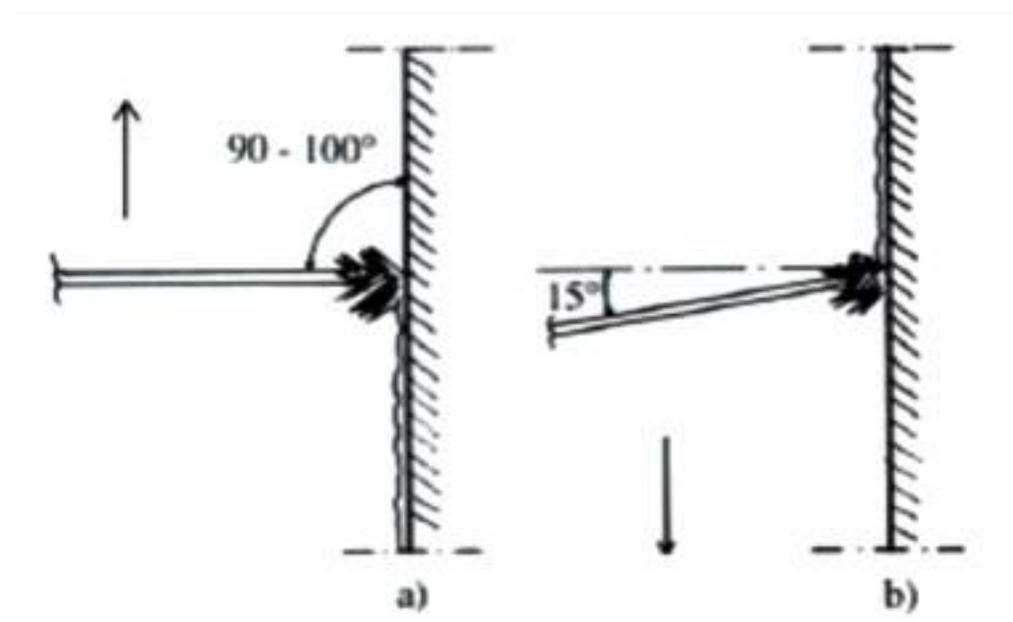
Posição do elétrodo para soldadura vertical.
